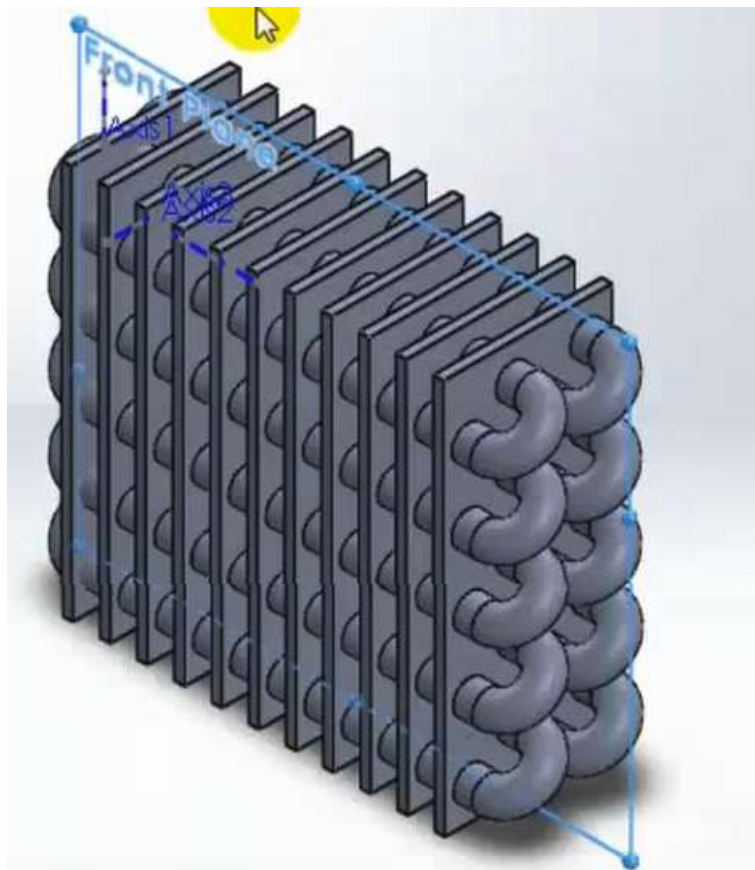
Готова модель трубчато-пластинчатого повітряного випарника.
